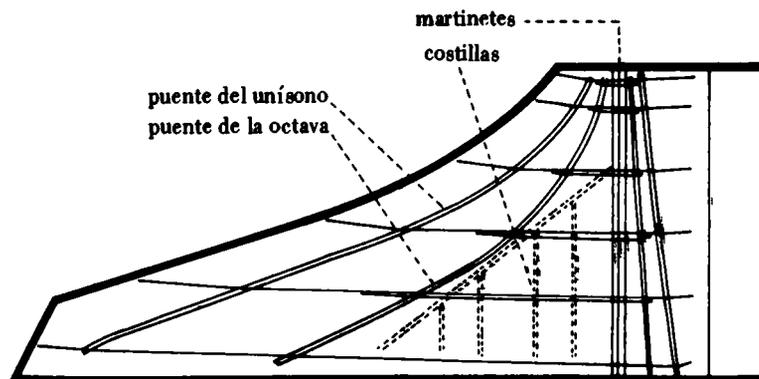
Planta de un clave flamenco. (Escala 1:20).
